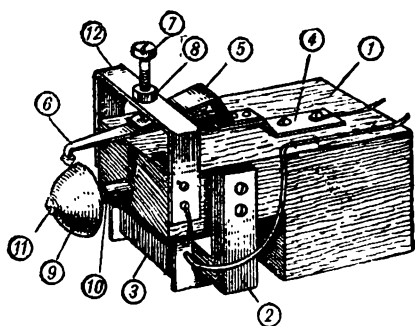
Самодельный электровзвонки и его части: 1 — деревянное основание; 2 — электромагнит; 3 — катушка электромагнита; 4 — якорь; 5 — контактная пластинка; 6 — молоточек; 7 — контактный регулировочный винт; 8 — контргайка; 9 — чашечка; 10 — стоечка; 11 — крепежный шуруп; 12 — контактная скоба.
